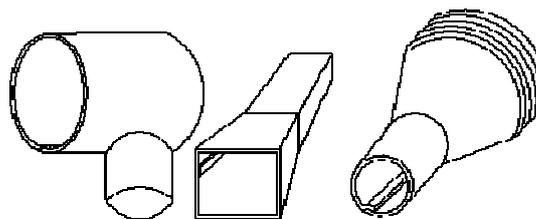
Общий вид корпусных деталей изделий космической техники
